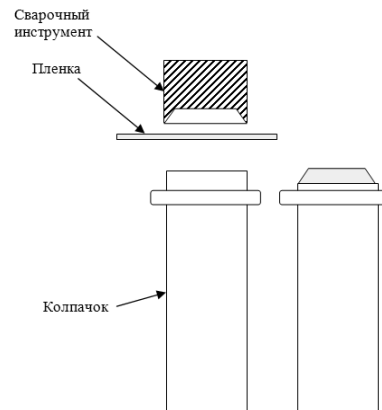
Схема сварки для сварочного инструмента с режущей кромкой диаметром 7,4 мм (СИ3)
